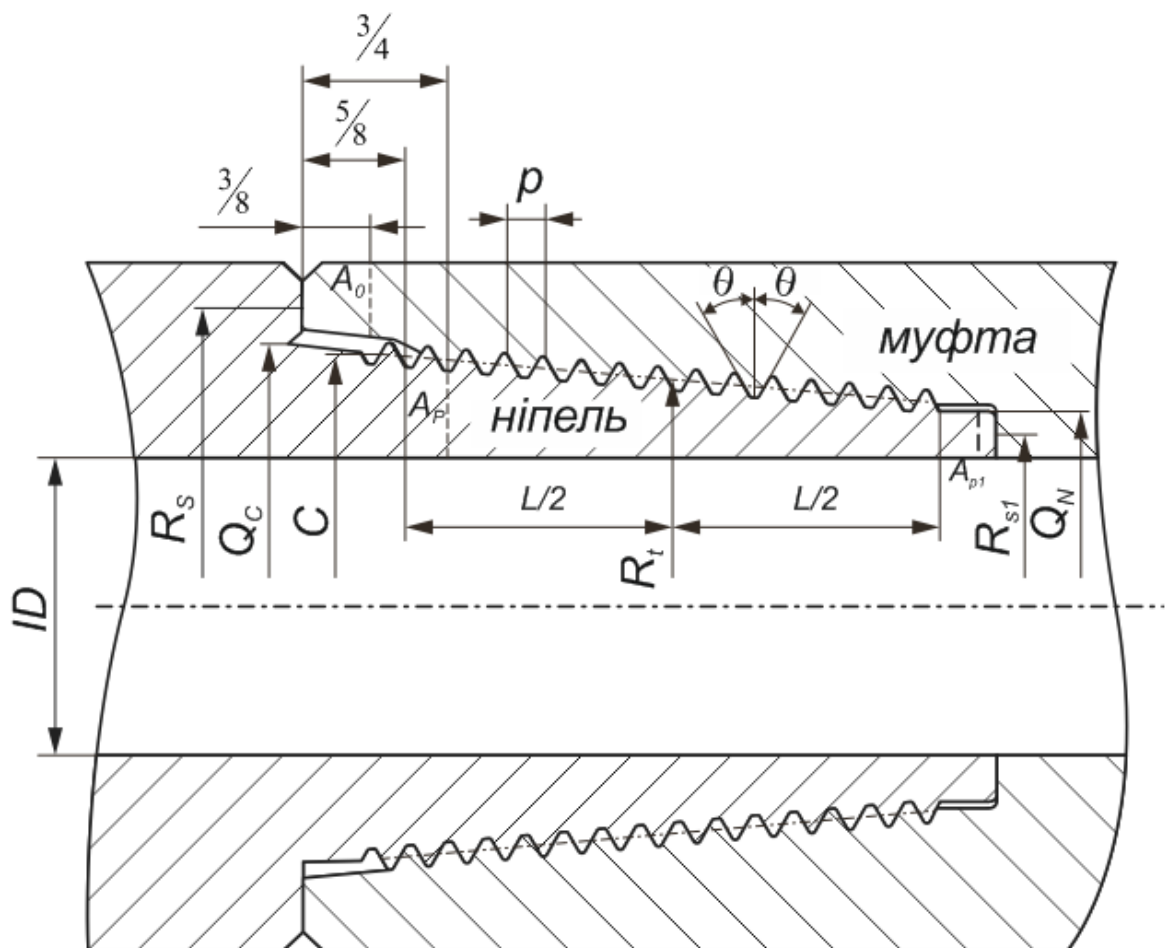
Розрахункова схема двоопорного з'єднання
